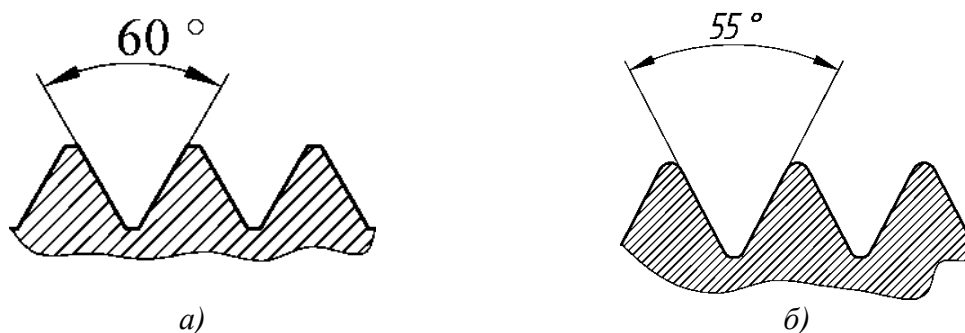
Профиль метрической (а) и трубной цилиндрической (б) резьбы
